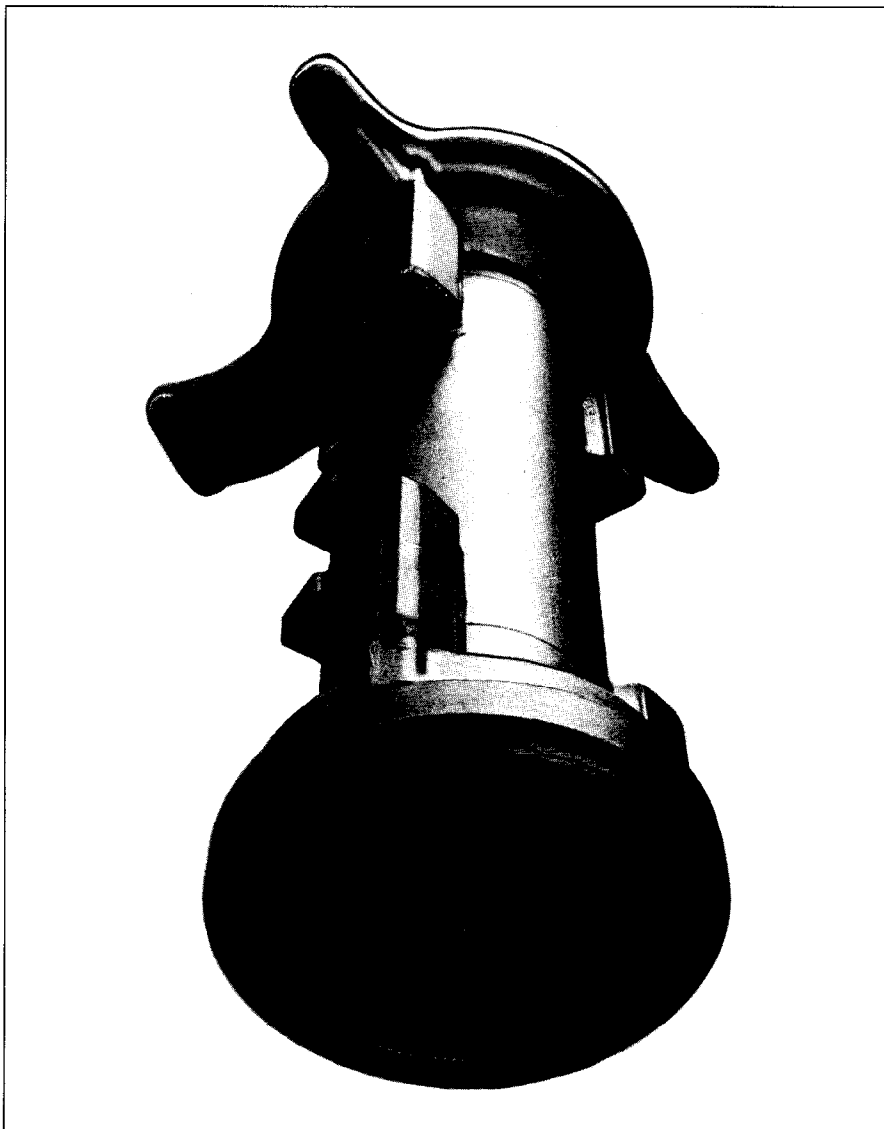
UP-Schweißen und Schutzgasschweißen: Getriebeaufnahmekörper für E-Lok-Antrieb (Stückmasse 211 kg, Länge 970 mm), Rohr aus St 45-3 N, Flansche und Anschläge aus RPSt 42-2 N, Schweißquerschnitt Rohrnahte $2 \times 14\,400 \text{ mm}^2$
